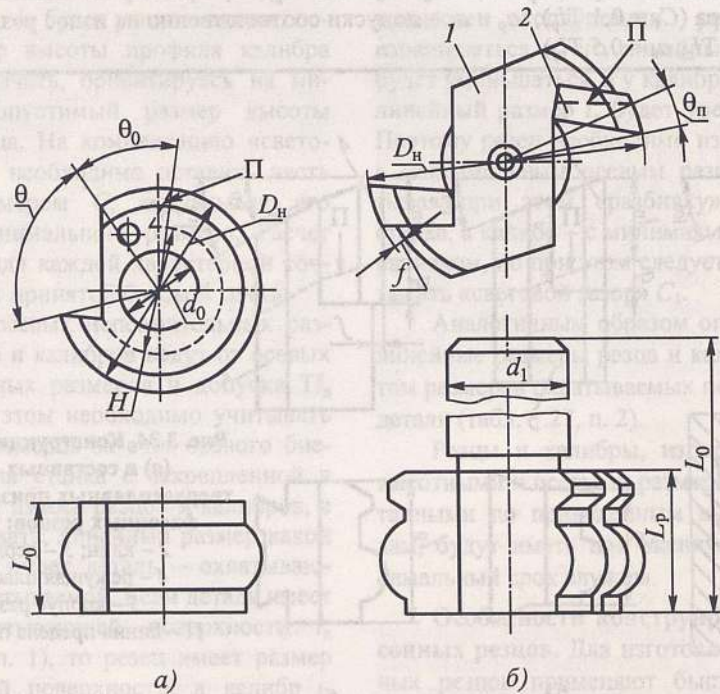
Конструкции цельного (а) и составного (б) твердосплавных круглых фасонных резцов: 1 – корпус; 2 – режущая пластина; П – линия предела переточки
